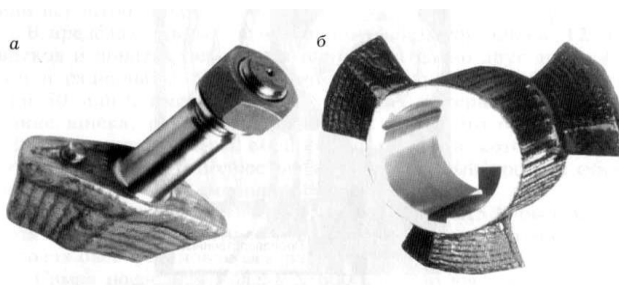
Рабочая лопатка корпуса(а) и съемная насадка (б)
